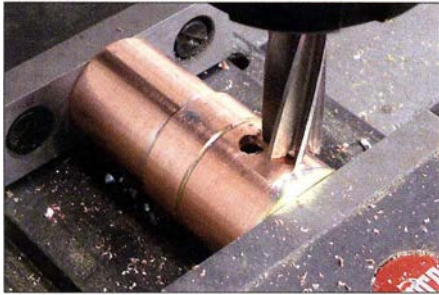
Planfräsen der Fläche für die SMA-Buchse
